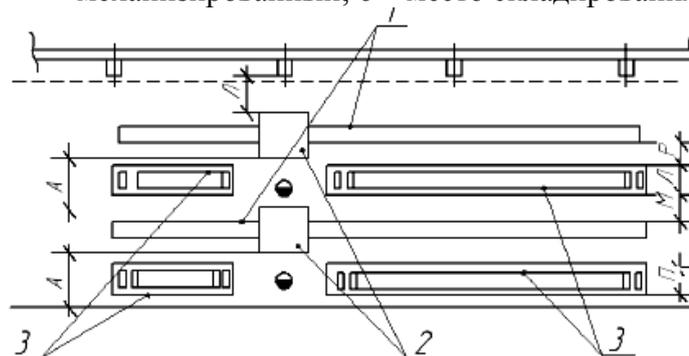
Размещение оборудования для электронно-лучевой сварки: 1 – моечно-сушильный агрегат; 2 – установка для размагничивания;
